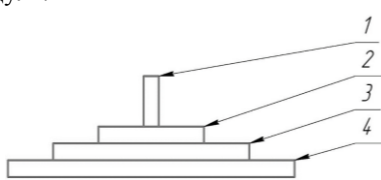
Схематический вид конструкции светодиодного светильника со встроенным ИК-обогревателем. Вид сбоку
